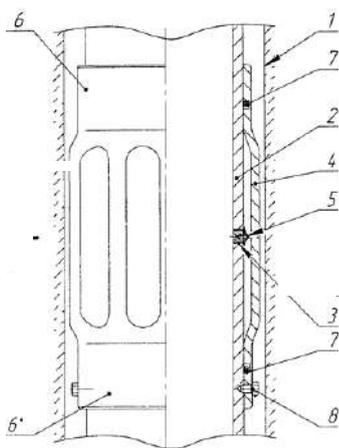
Центратор гидравлический [7]: 1 – ствол скважины; 2 – корпус; 3 – радиальные каналы; 4 – центрирующие элементы; 5 – средство перевода центрирующих элементов в рабочее положение; 6 – гофрированные трубы с кольцевыми зауженными каналами; 7 – самоуплотняющиеся манжеты; 8 – винты
